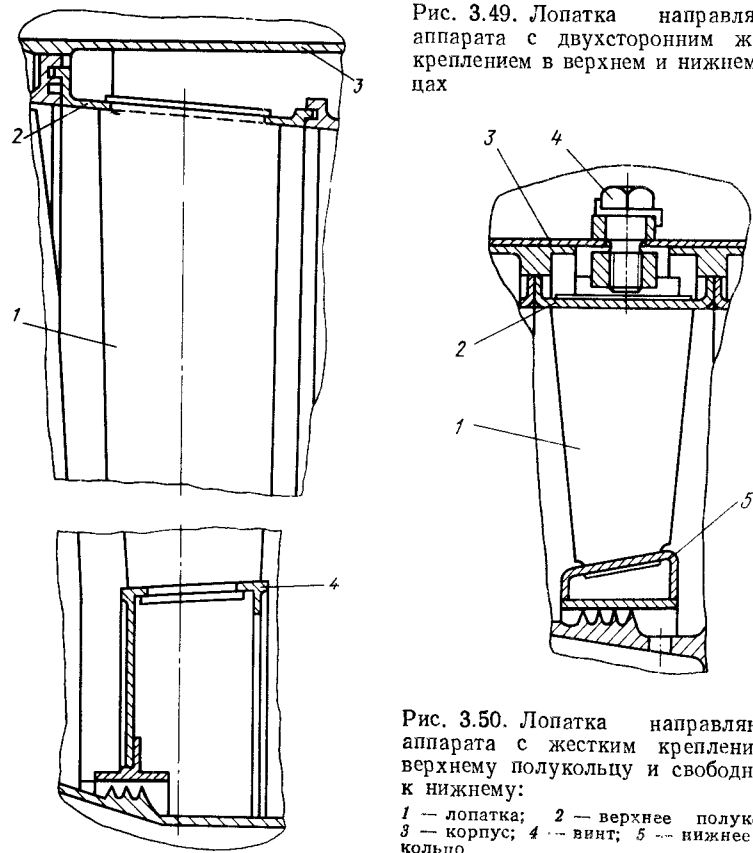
Лопатка направляющего аппарата с двухсторонним жестким креплением в верхнем и нижнем кольцах
